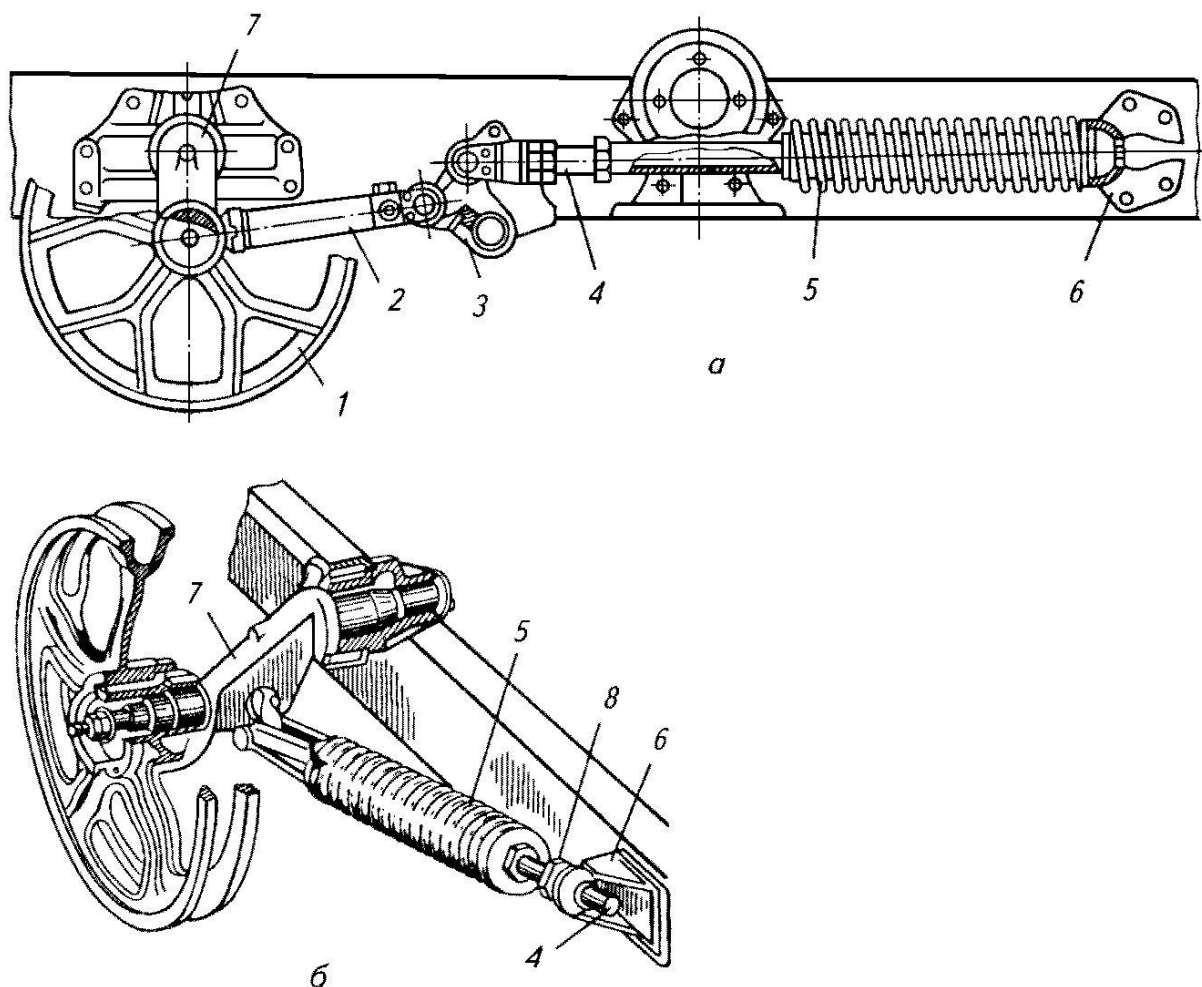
Натяжное устройство с кривошипом (коленчатой осью):
